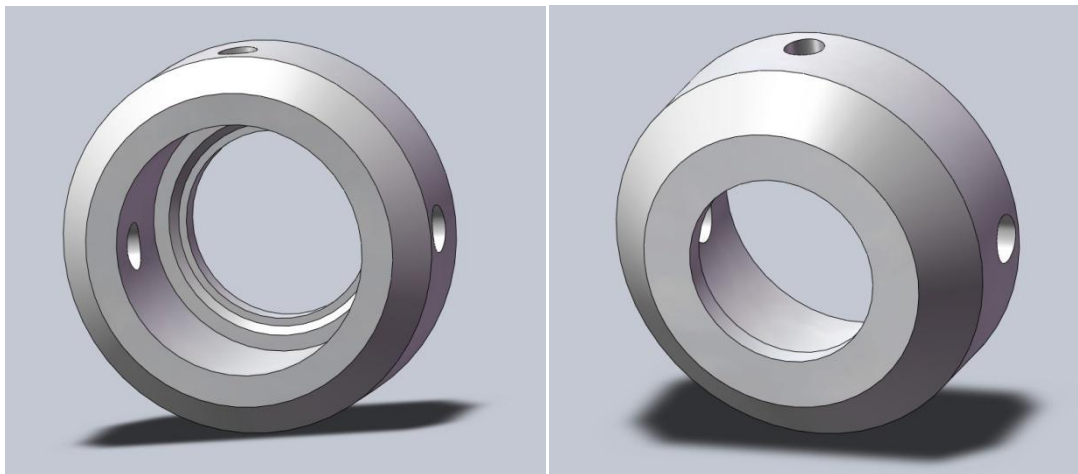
(a) e (b) - Desenho CAD do Casquilho do Rolamento (Ertalon 66SA , Frente e Verso)
